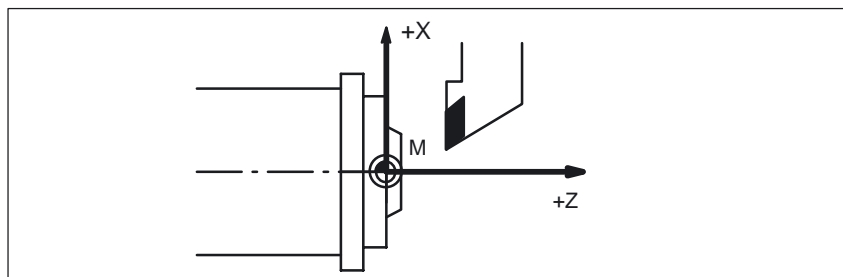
MKS mit den Maschinenachsen X, Z (Drehmaschine)
